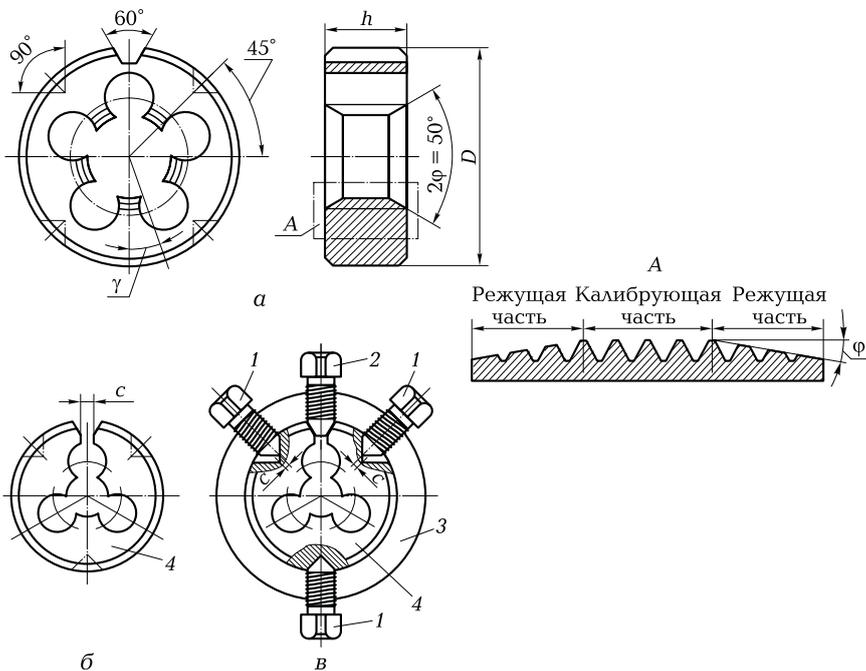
Резьбонарезная плашка для нарезания резьбы:
